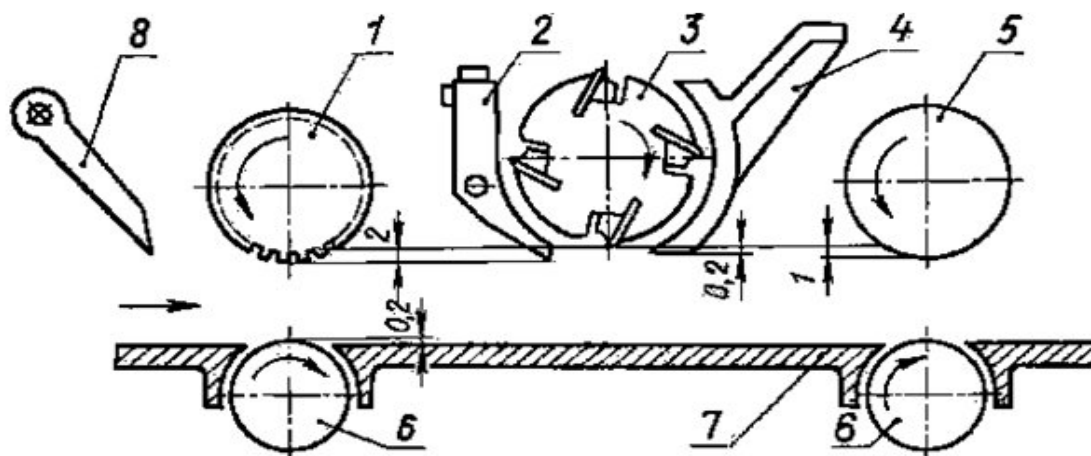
Схема розташування деталей одностороннього рейсмусового верстата:
